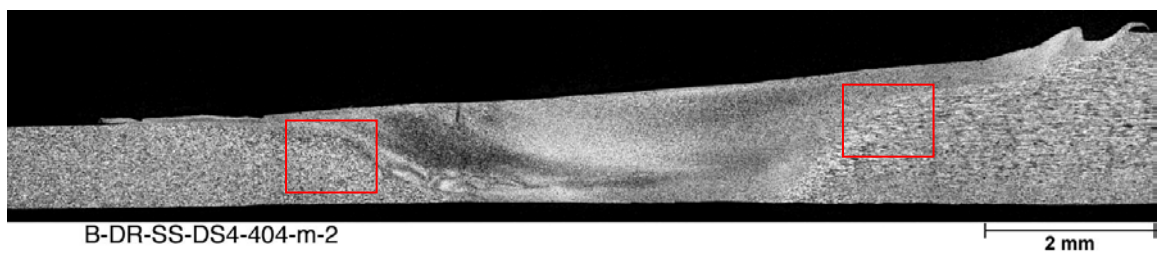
Macrografia de uma junta 5754 H22 soldada com 5 m/min. Ataque químico: Barker.
